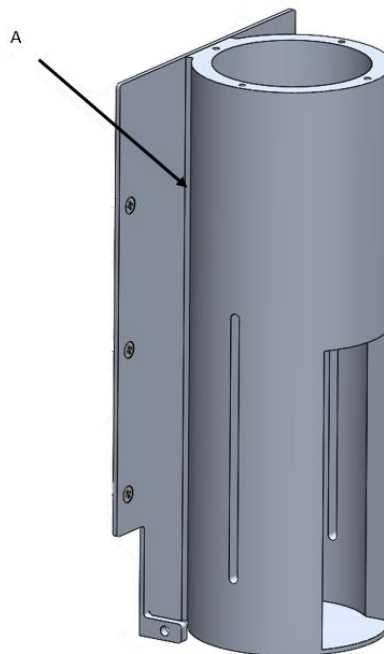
Ligação entre estrutura tubular e parede de fixação.
